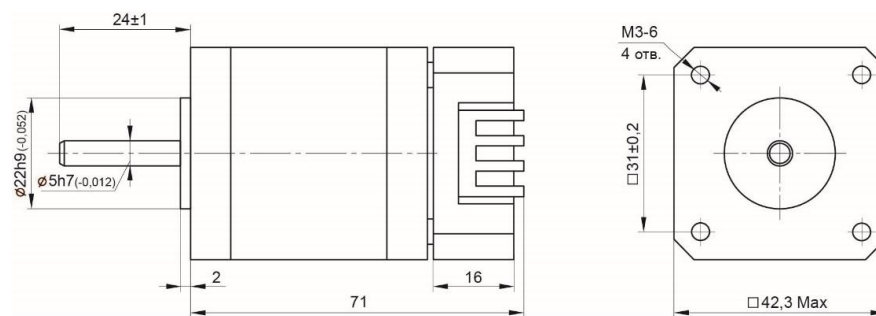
Габаритные размеры и присоединительные размеры устройства.
